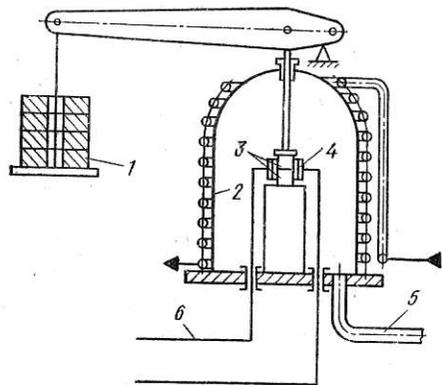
Схема диффузионной сварки в вакууме
